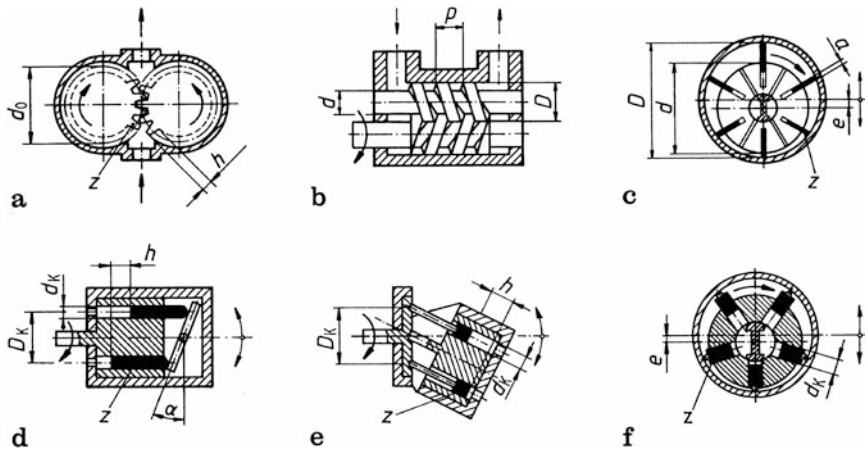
Prinzipbild zur Berechnung des geometrischen Fördervolumens der Verdrängermaschinenbauarten nach VDI 2152. a Zahnradpumpe mit Außenverzahnung; b Schraubepumpe; c Einhubige Flügelzellenpumpe; d Axialkolbenpumpe, Schrägscheibe; e Axialkolbenpumpe, Schrägachse; f Radialkolbenpumpe mit Außenexzenter
